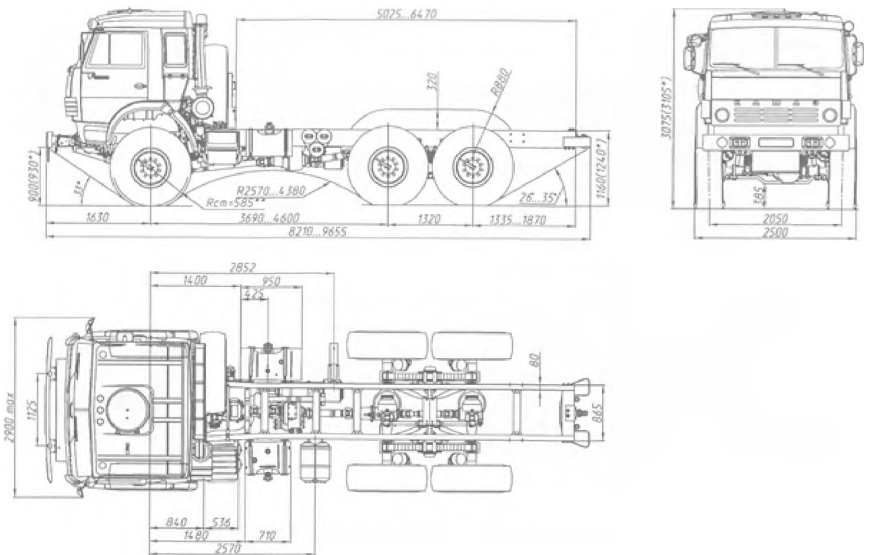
Шасси автомобиля-тягача КАМАЗ-53501. Габаритные размеры.
